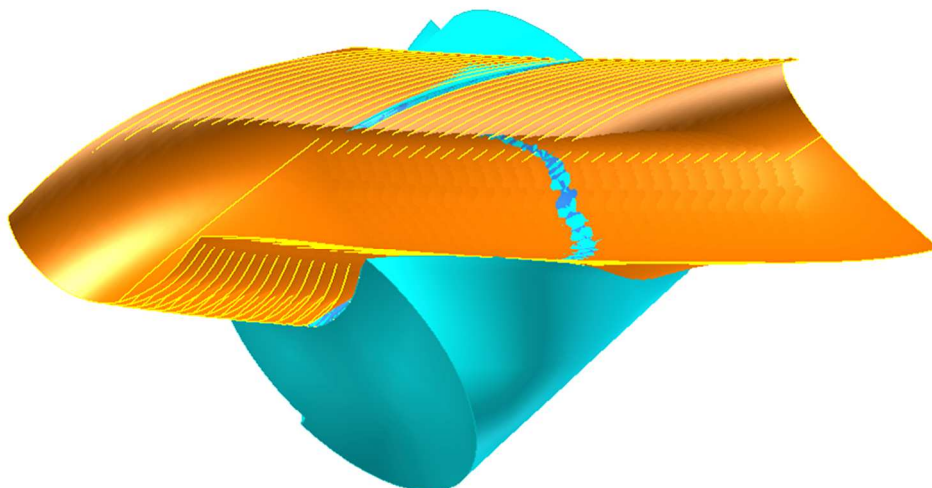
Положення гвинтової поверхні канавки свердла при її обертанні
